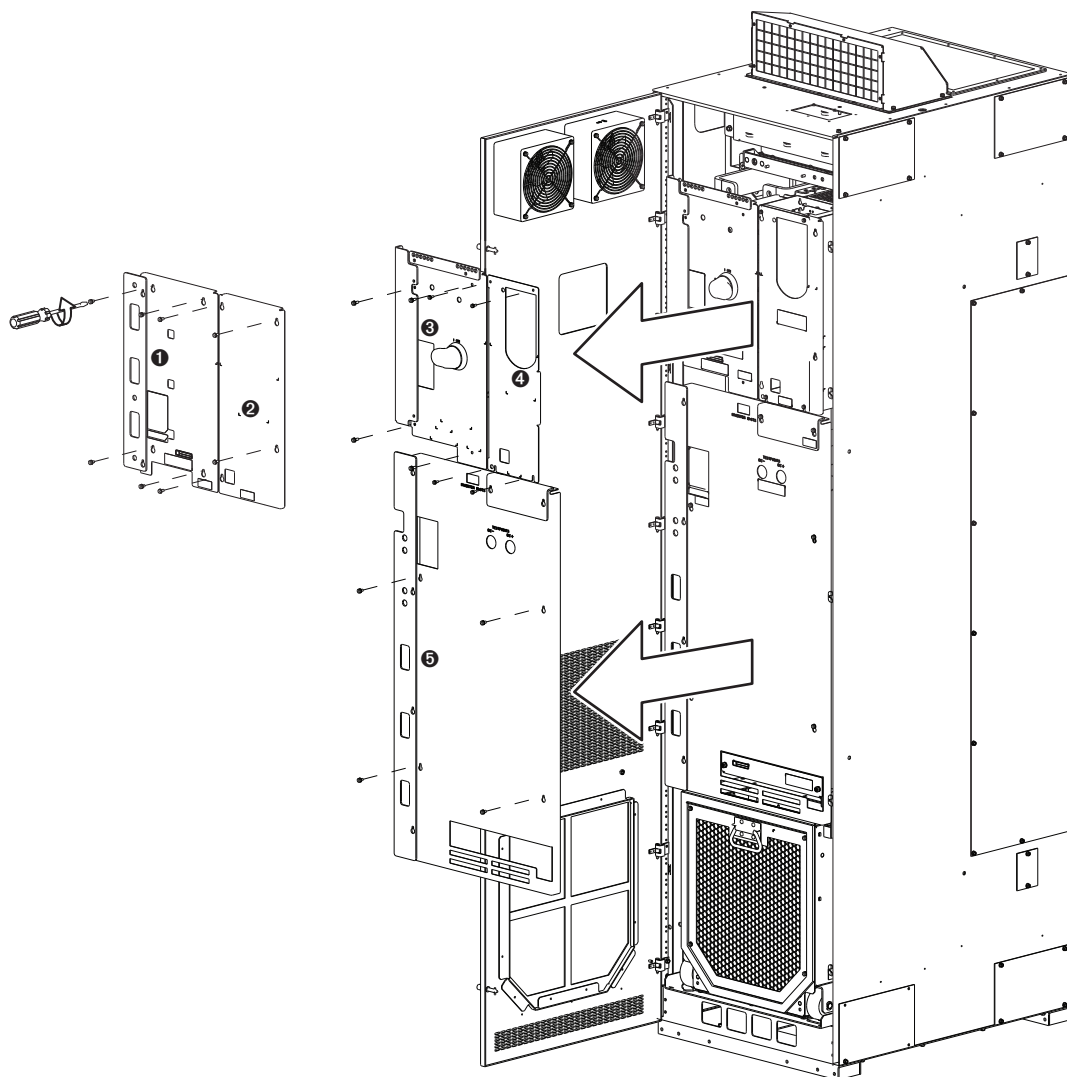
Коды корпуса В, L, P, W (IP20, NEMA/UL Type 1), дверца доступа к шкафу привода
